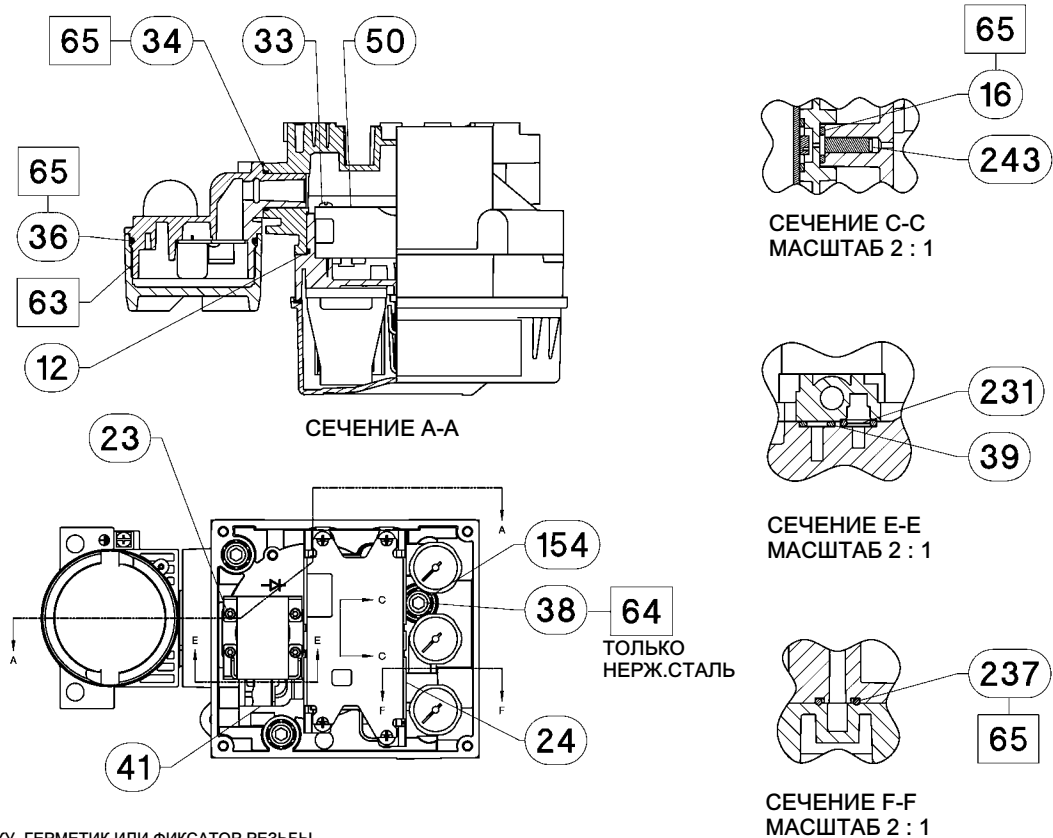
2. Корпус цифрового контроллера клапана FIELDVUE DVC6200 СПАЗ в сборе
